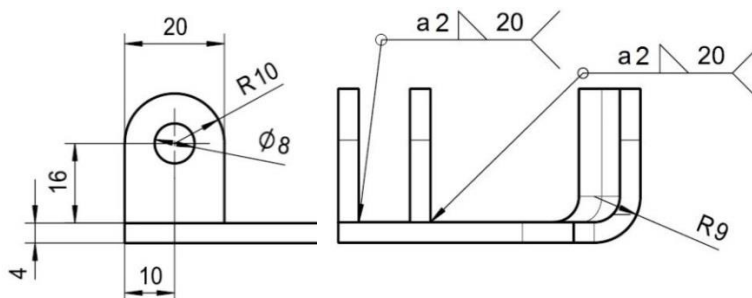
; Schweißbedingung an der Aufnahme vom Viereckenscharnier
